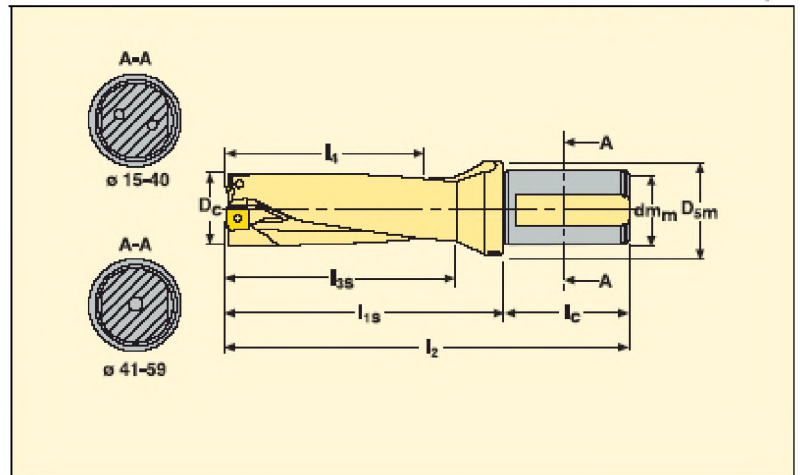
Свердло зі змінними твердосплавними пластинами SD503-21-59-25R7
